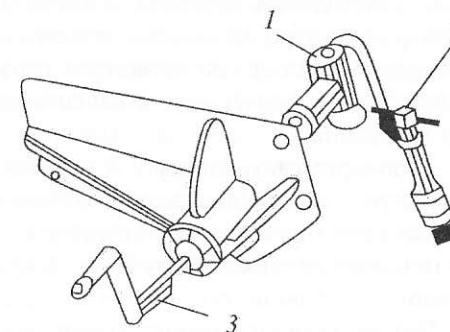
Ручний пристрій: 1 – редуктор РП-60-860; 2 – пристрій для розгальмування рульового приводу РП-60-ІА; 3 – рукоятка ручного приводу
